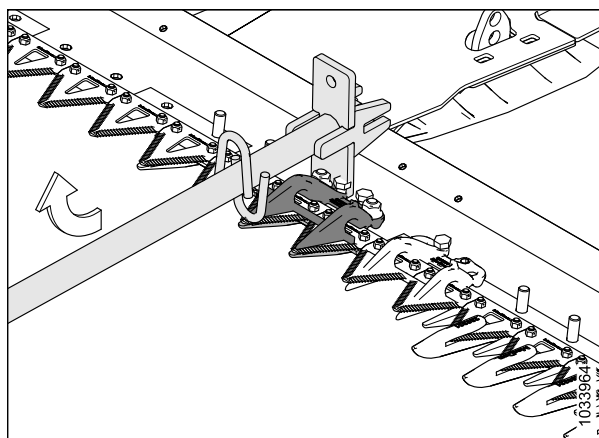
Регулировка смещением вверх — укороченный противорезающий палец
